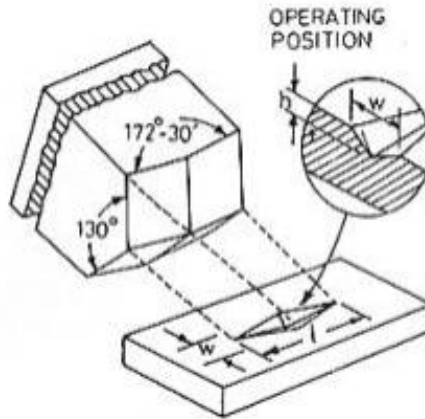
Penetrador Knoop y dimensiones principales de la impronta
